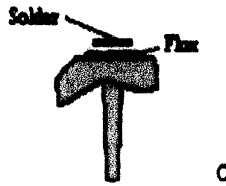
Líquido para soldar y un pequeño trozo de soldadura.
